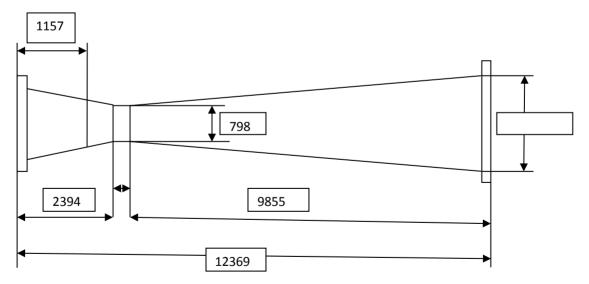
Venturi para colocar en el ducto de Planta Nueva a la entrada del ciclón lavador
